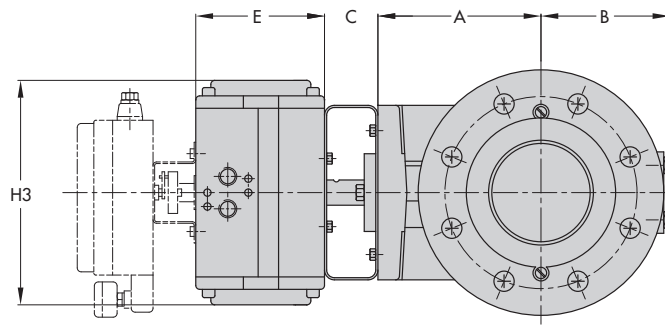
· Disegno dimensionale Tipo 3310/BR 31a
